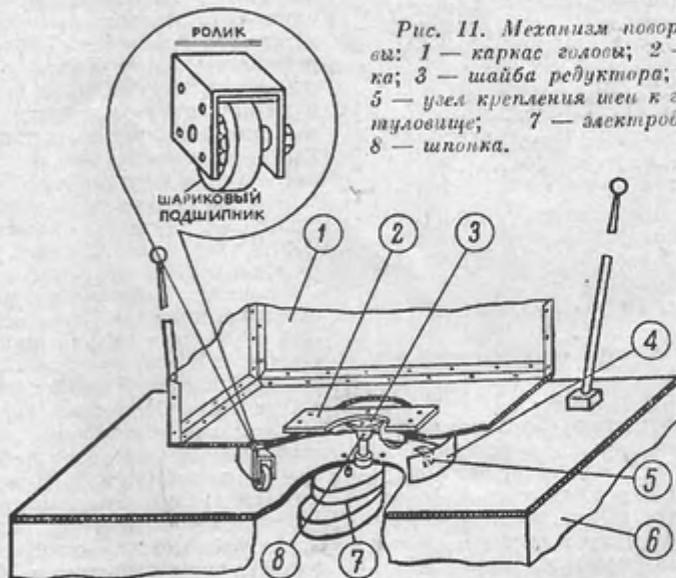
Механизм поворота головы: 1 — каркас головы; 2 — накладка; 3 — шайба редуктора; 4 — шей; 5 — узел крепления шей к голове; 6 — туловище; 7 — электродвигатель; 8 — шпонка.
